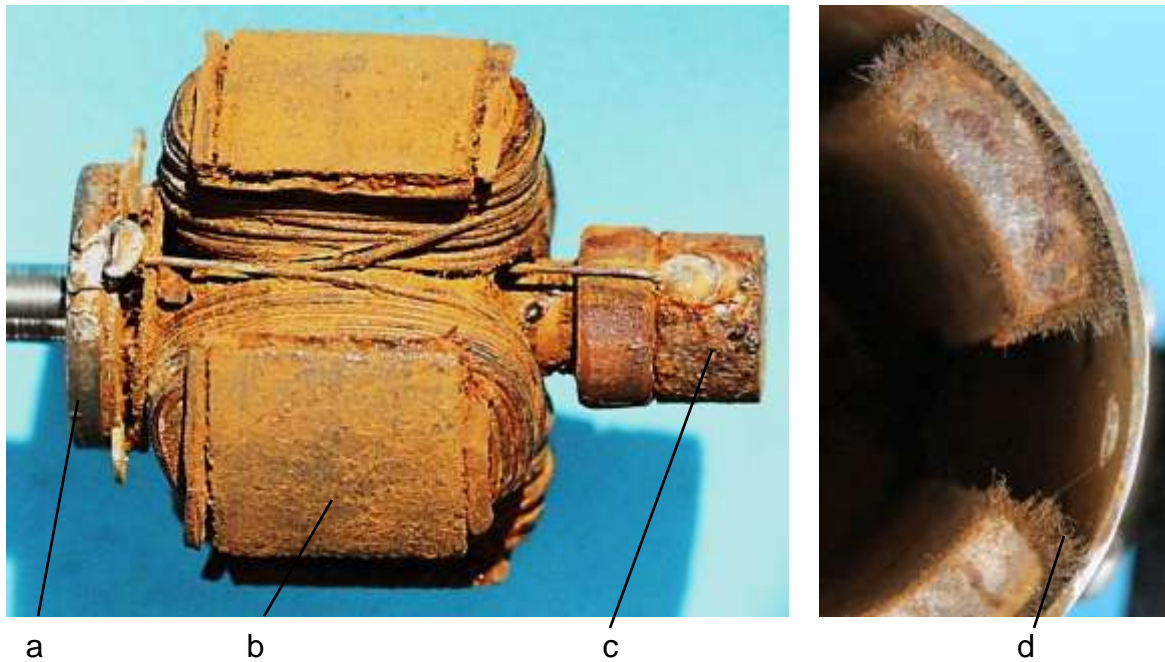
Stark korrodierter Innenraum: a) Massekontaktscheibe, b) Blechpaket (Durchmesser 33 mm), Länge 15 mm, c) Spannung führender Anschluss, d) Eisen-späne
